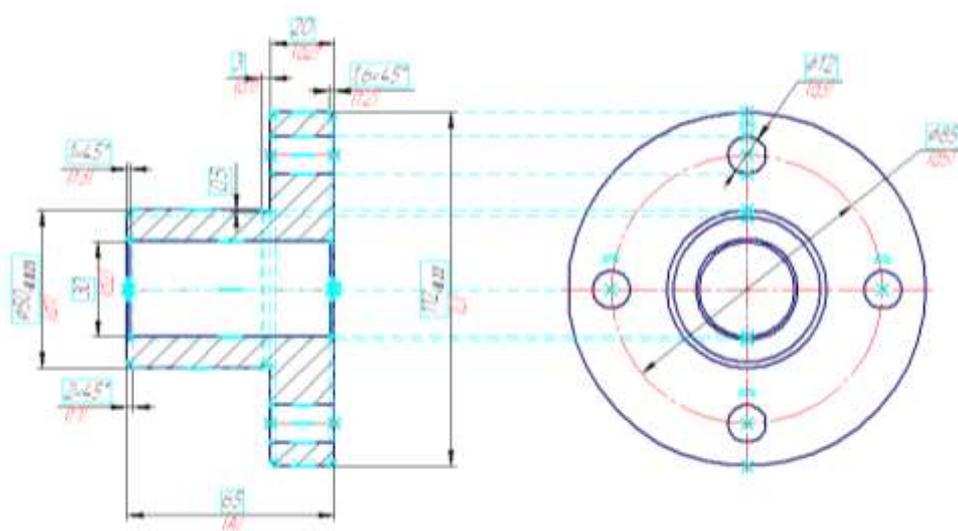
Главный вид и сечение детали Фланец с привязками (вариант)
